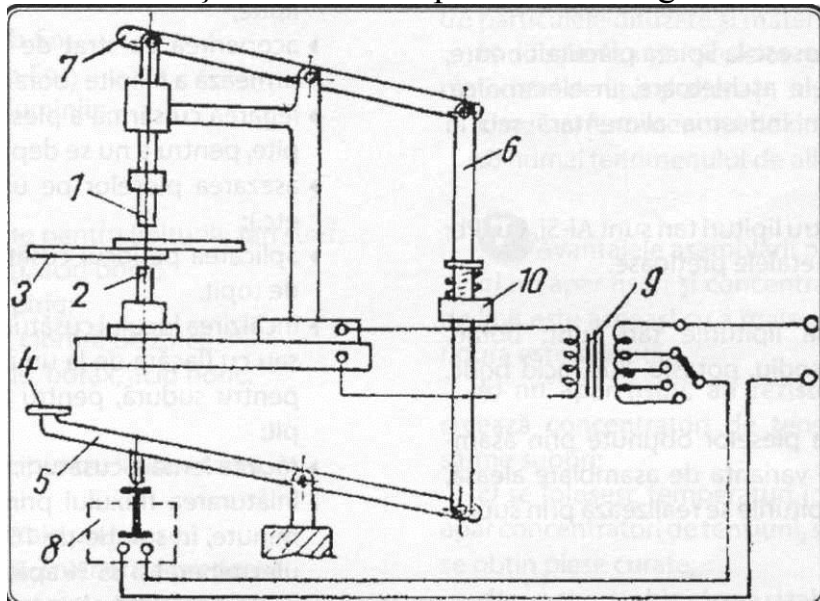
Instalație de lipire prin rezistență de contact: 1,2- electrozi din cărbune sau cupru; 3 - piese de lipit; 4 - pedala de acționare pentru realizarea presiunii de contact; 5, 6, 7 - pârghii pentru transmiterea forțelor de presare; 8 - contactori; 9,10 - transformator de curent electric.
